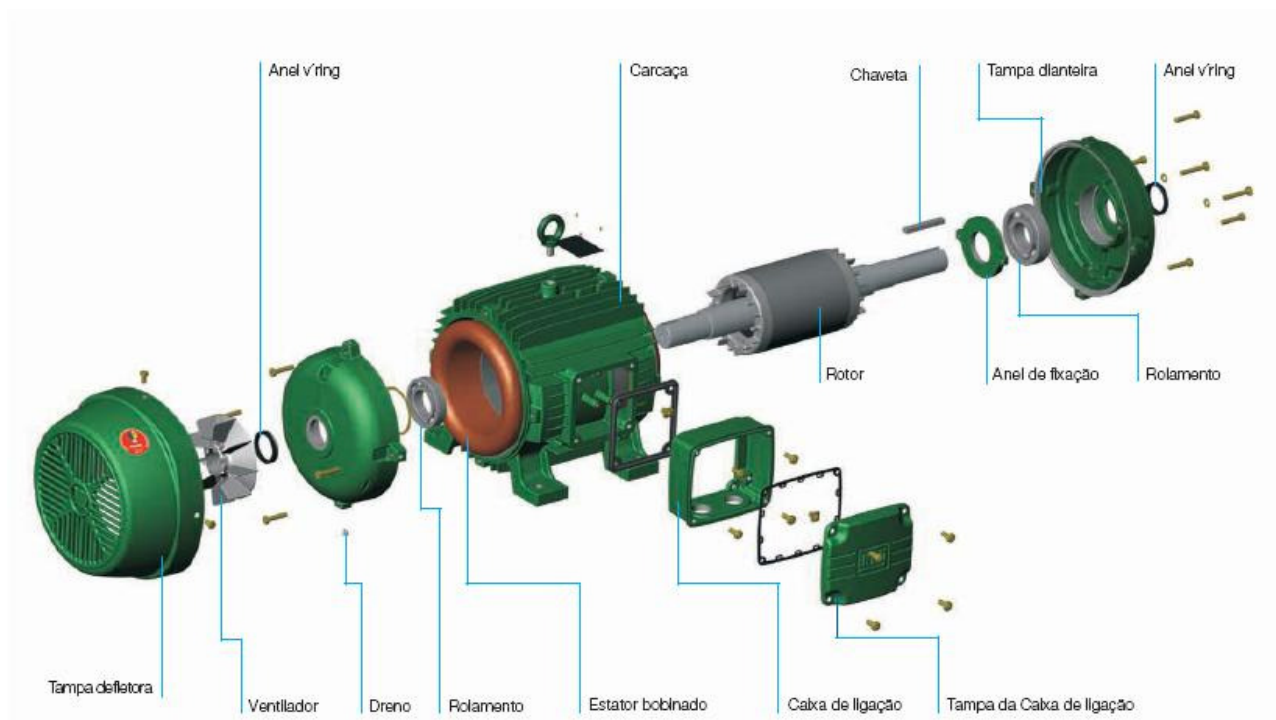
Vista explodida de um motor de indução trifásico com rotor em gaiola.
